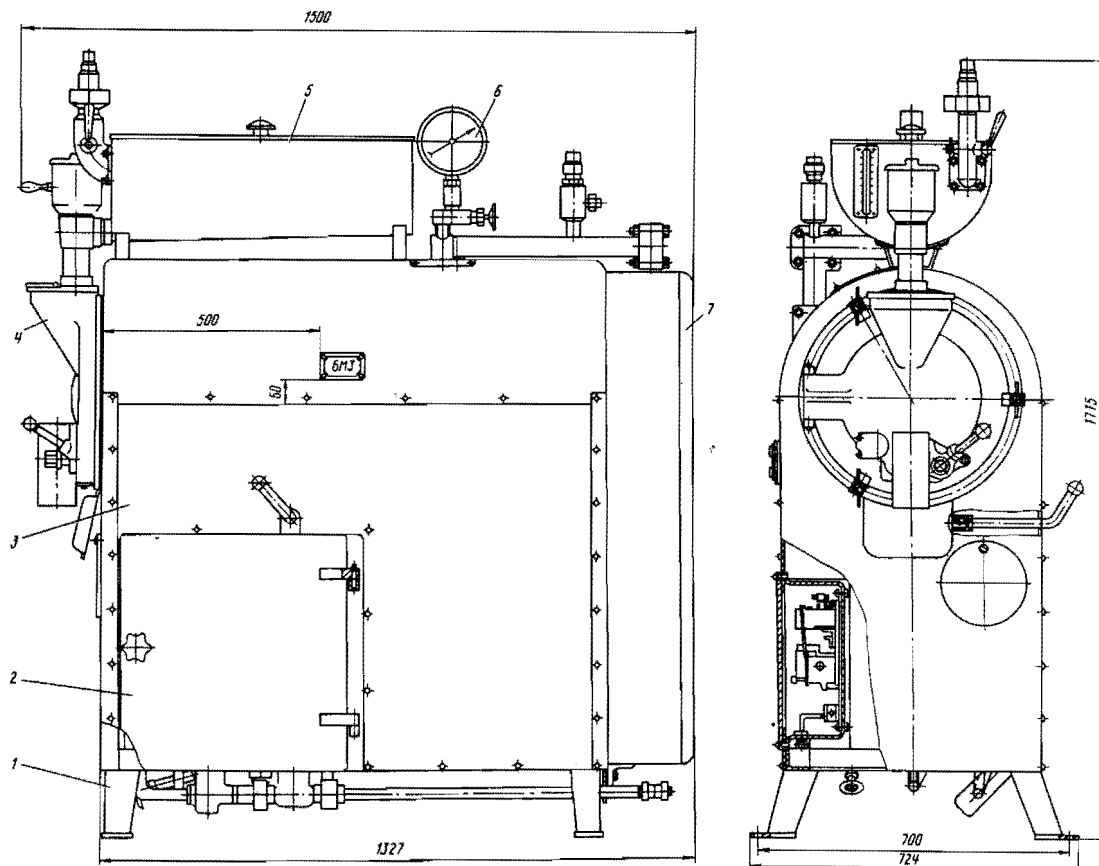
Общий вид фризера марки ОФА-М для мороженого:
